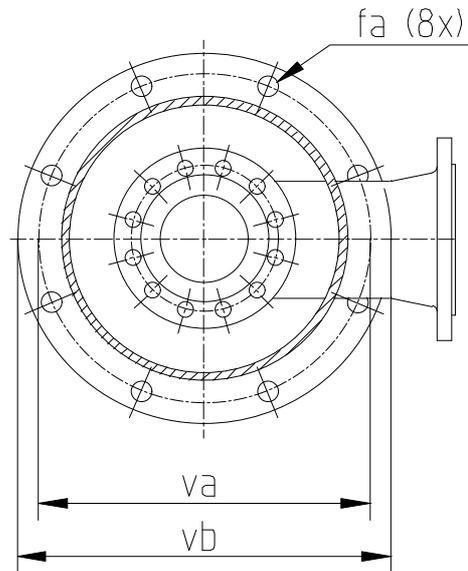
Abmessungen der Fußpads (Draufsicht).
